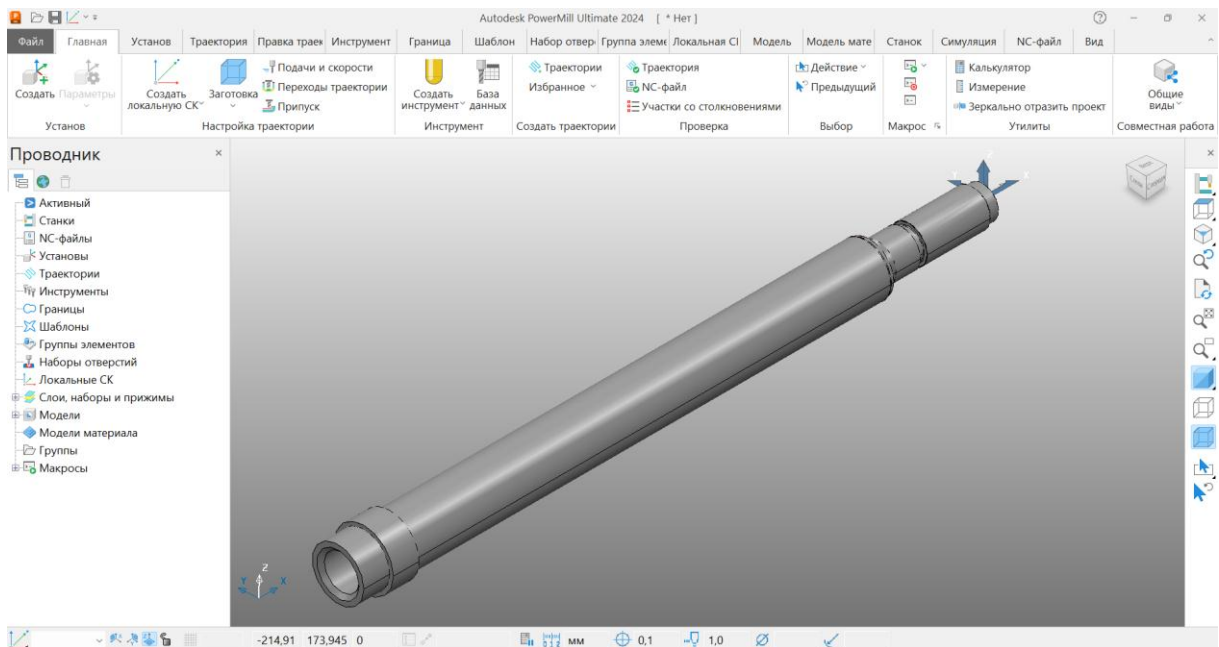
Модель деталі, імпортована в PowerMill
